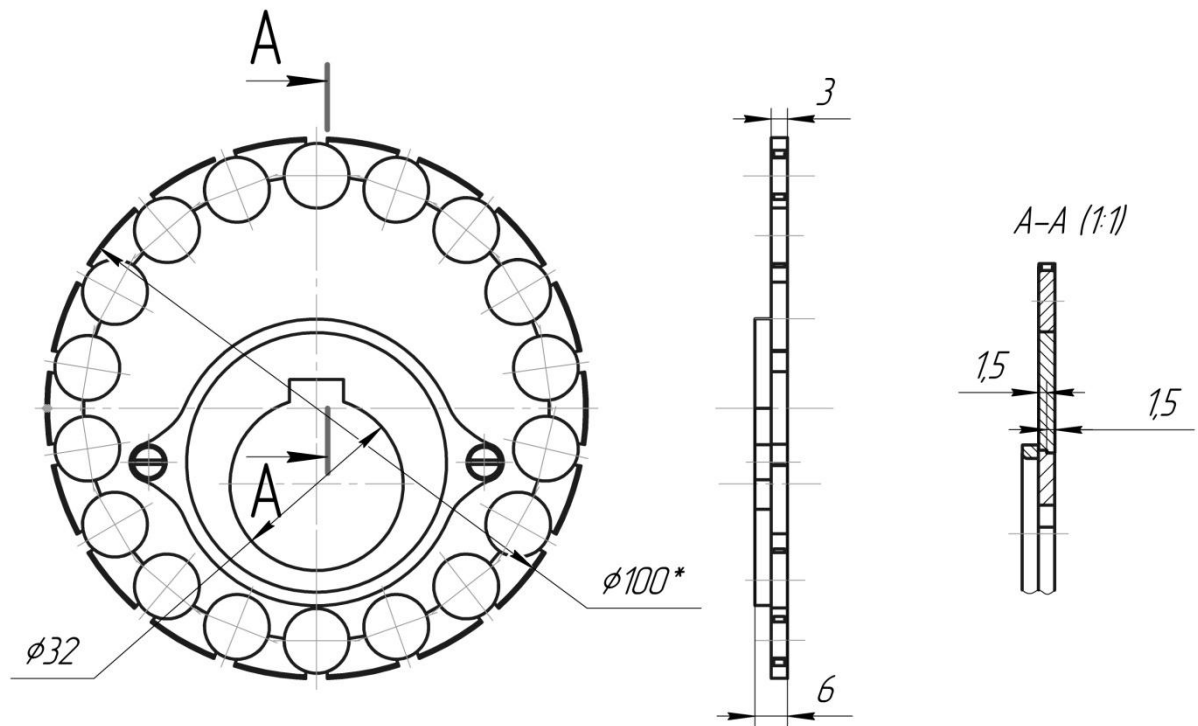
Основні розміри модернізованого дискового інструмента
